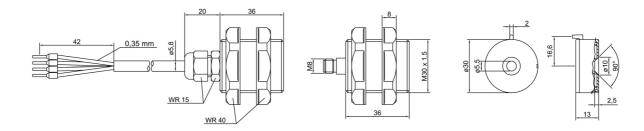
Dimensioni sensore ed attuatore MC330x
